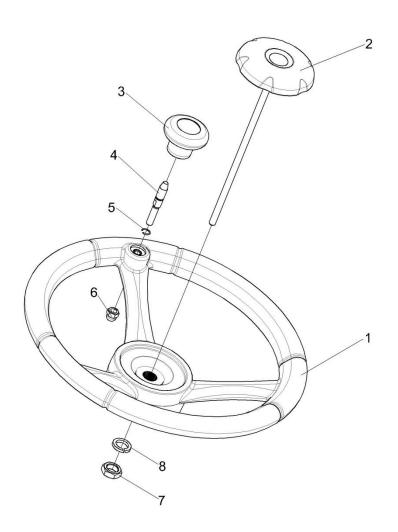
Установка колеса рулевого КЗК-12-0122300
